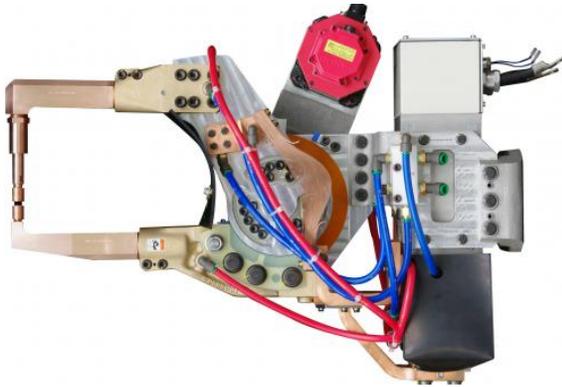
Servo Gun (herramienta incorporada en robot)
